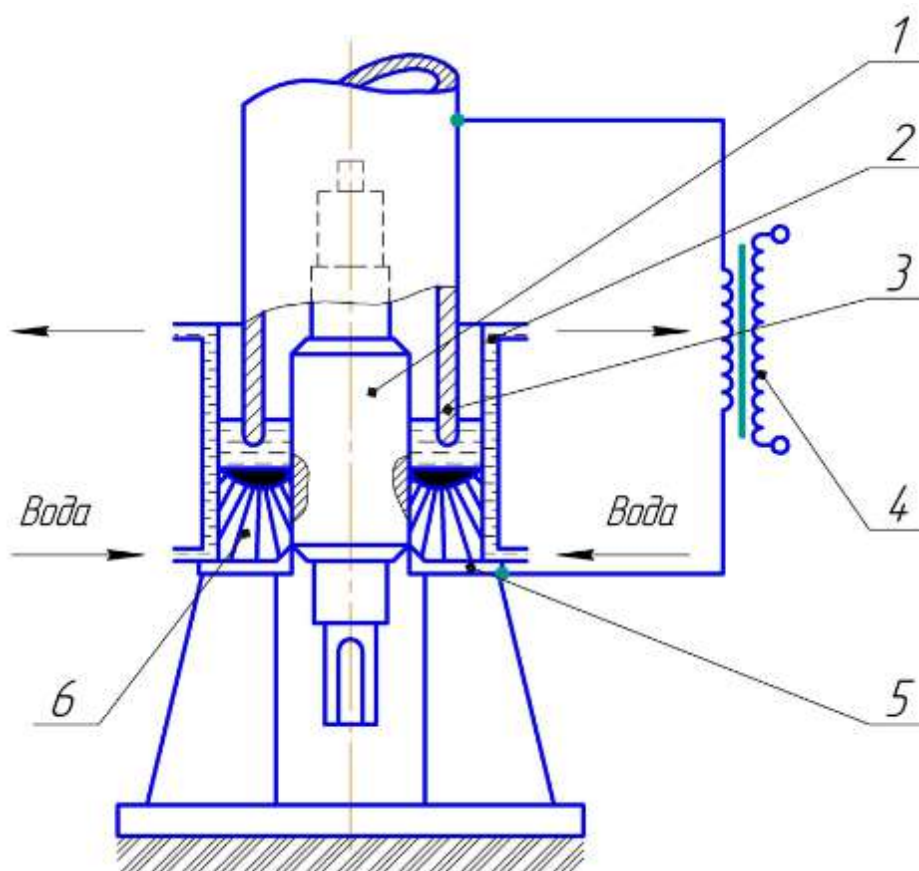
Наплавлення прокатних валків електродом-трубою: 1 – наплавлюваний прокатний валок; 2 – кристалізатор; 3 – електрод-труба; 4 – трансформатор; 5 – стартове кільце; 6 – наплавлений шар
